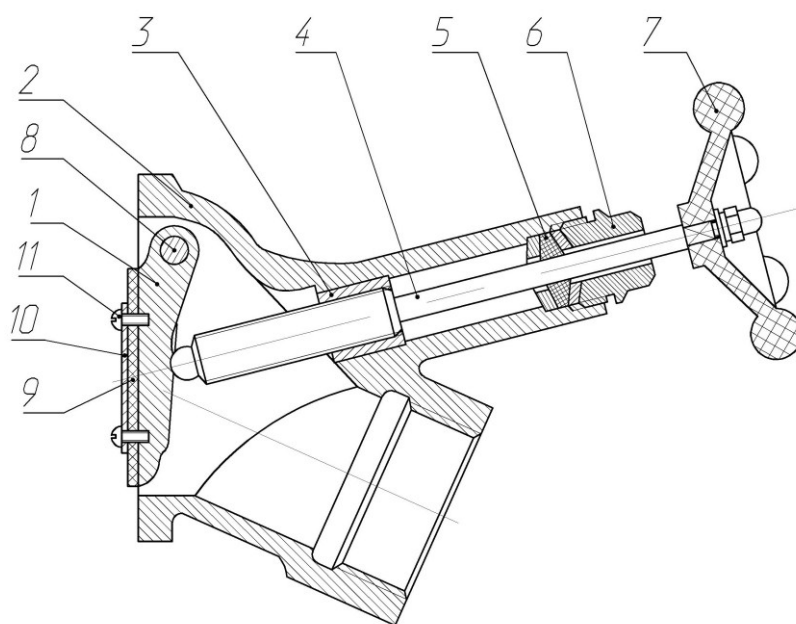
Задвижка насоса ПН-40УВ: 1-клапан; 2-корпус; 3 - втулка; 4-винт (шпиндель); 5-уплотнение; 6 - гайка; 7 – маховик; 8 – ось клапана; 9 – подушка клапана; 10 – накладка; 11 - винт.
